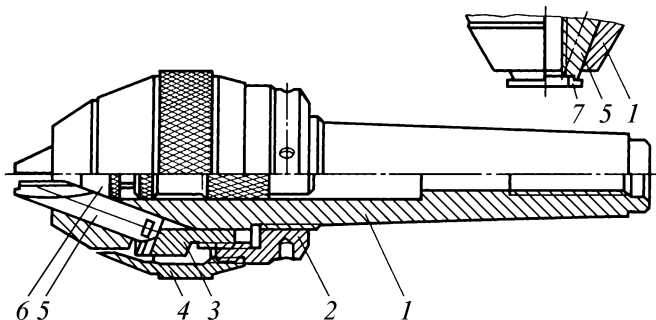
Сверлильно-фрезерный патрон "Спутник"
